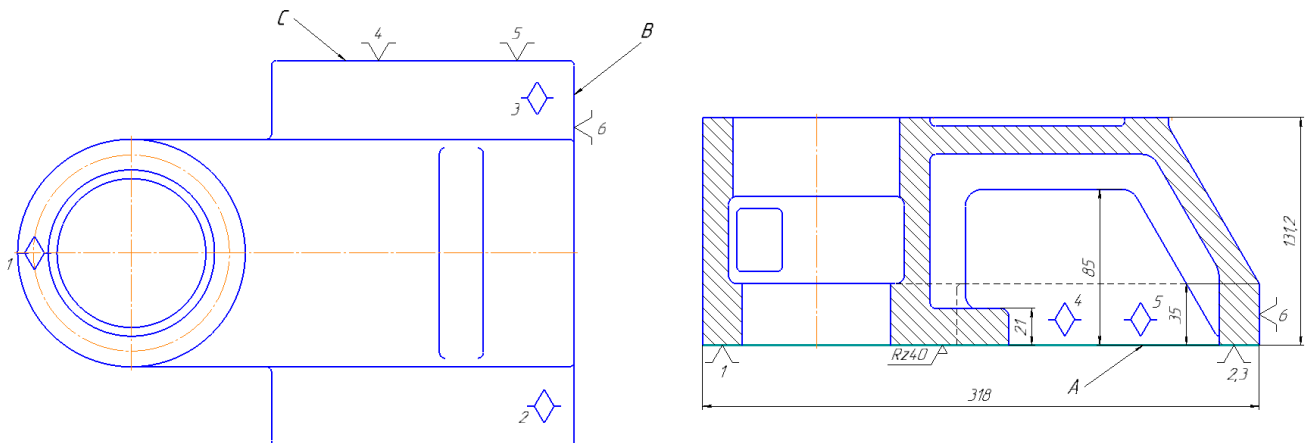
Схема базування та закріплення заготовки на операції 020 фрезерна
